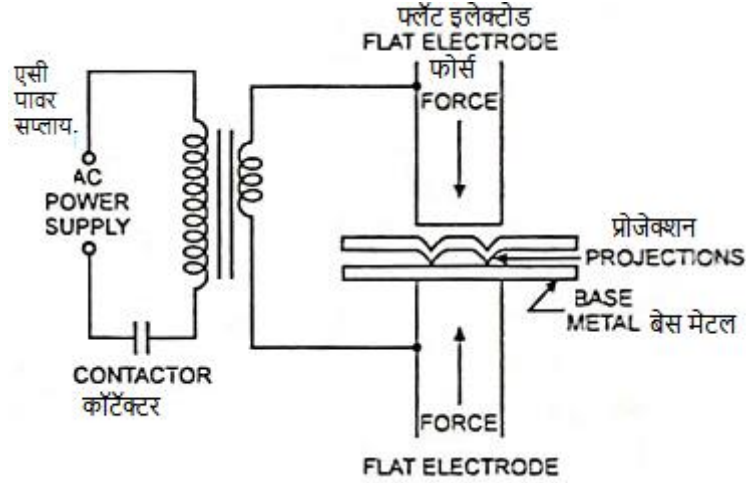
प्रोजेक्शन वेल्डिंग (Projection Welding)
